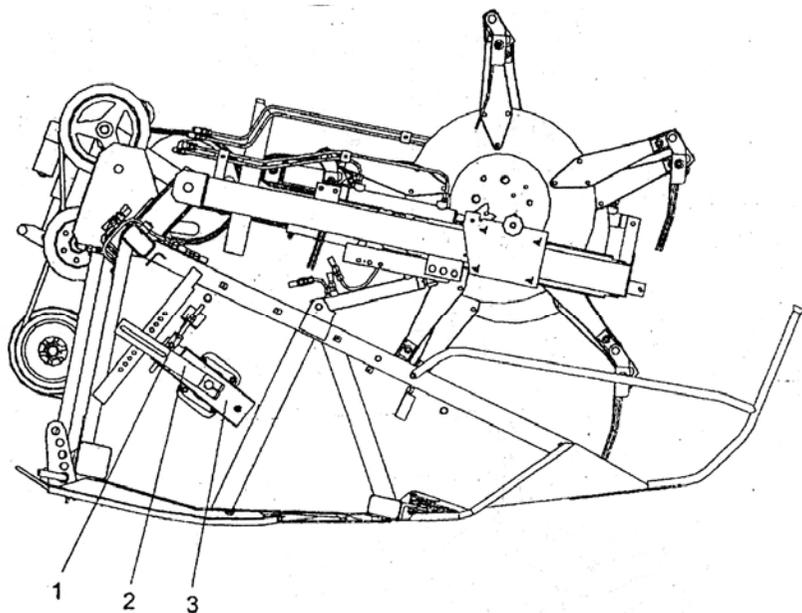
Установка шнека жатки: 1 — тяга; 2 — рычаг; 3 — опора шнека
